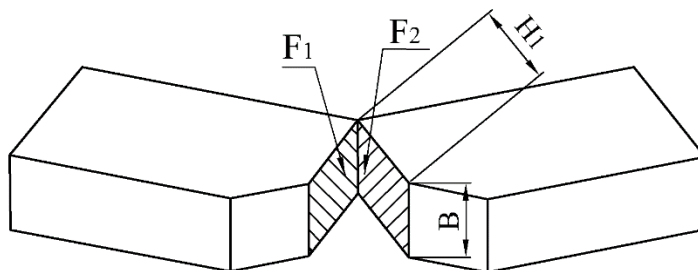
Надрезанный образец после испытания на ударный изгиб
